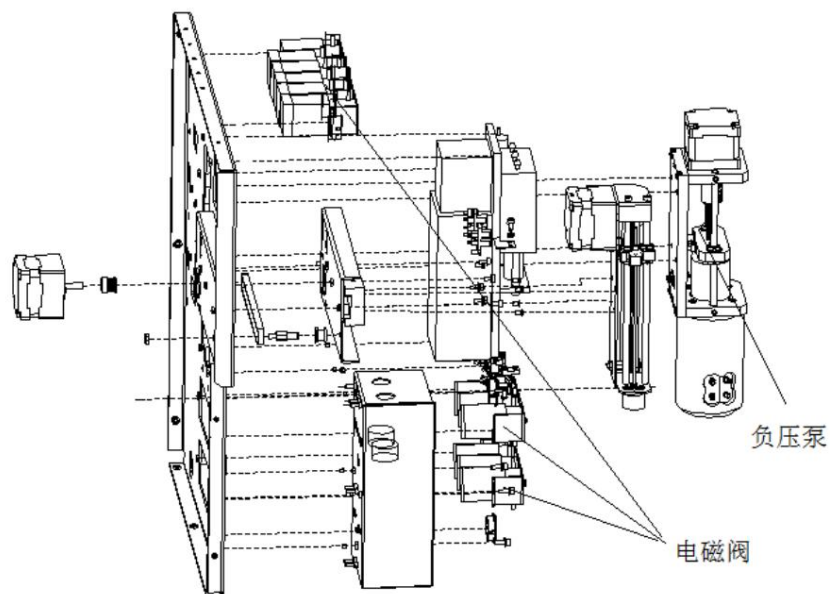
Démontage complet des composants de la carte de circuit imprimé hydraulique
